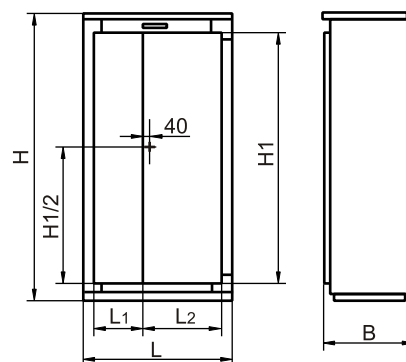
Шкафы ШД5, ШД0 с двустворчатой дверью
